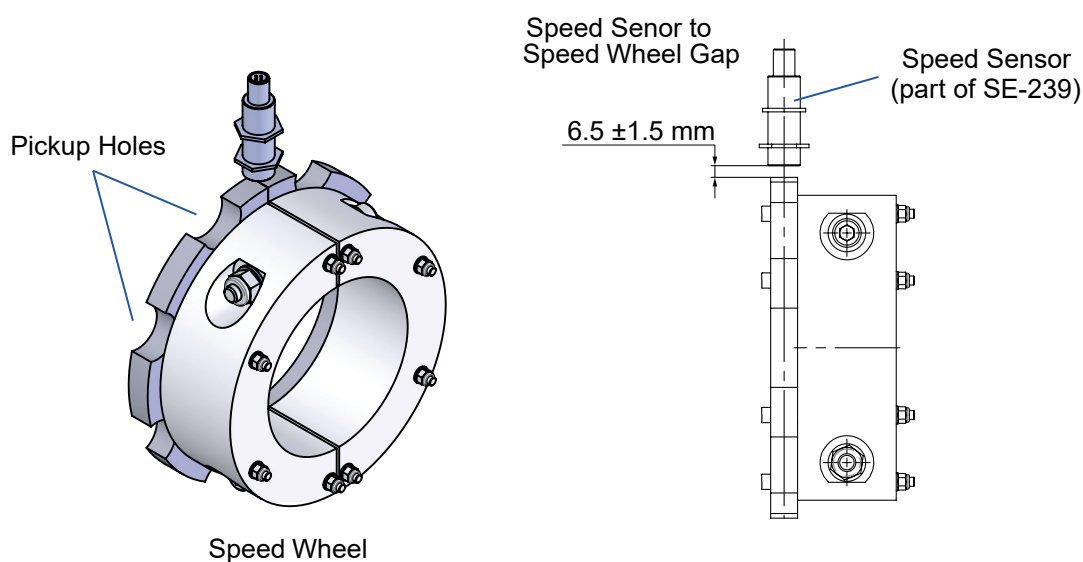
Cablaggio (SE-239) per sensore giri e ruota fonica
